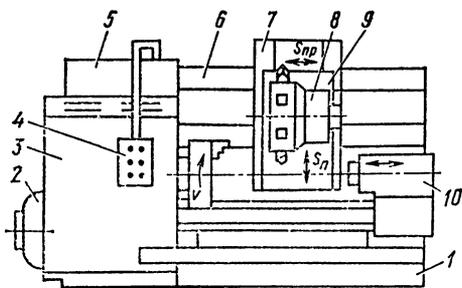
Общий вид токарно-винторезного станка с ЧПУ
